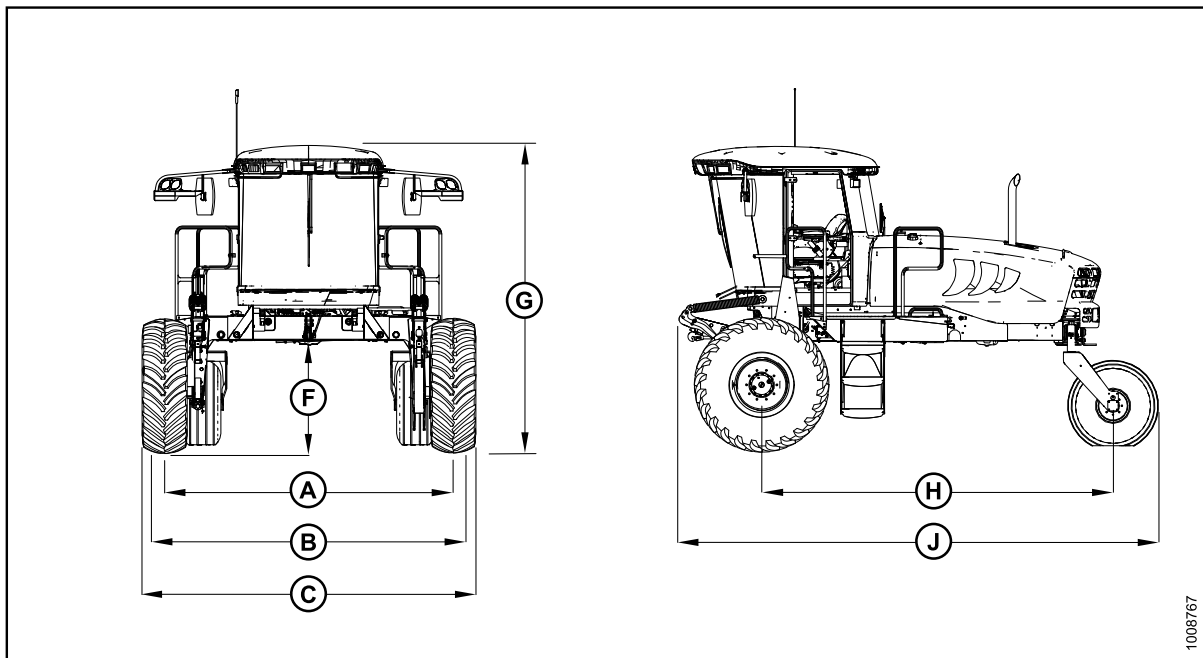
Размеры валковой косилки — Передняя часть
